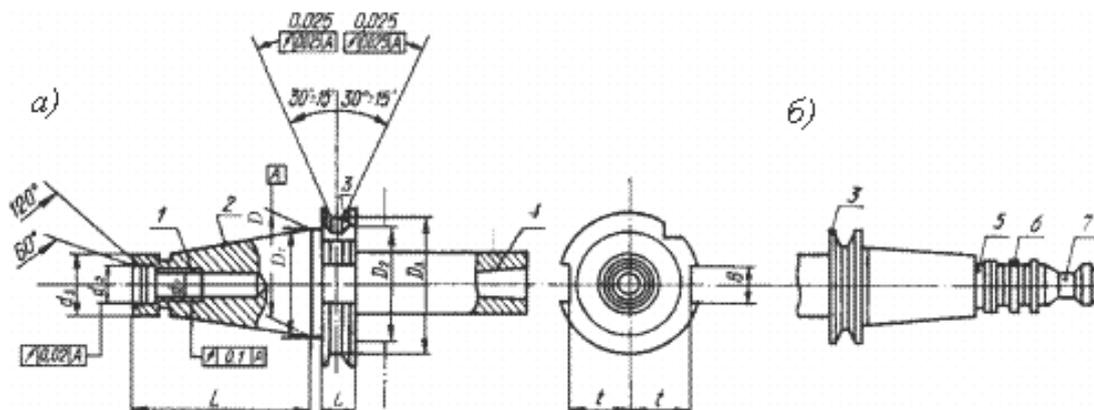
Оправка для многоцелевых станков с ЧПУ: а – хвостовик; б – хвостовик с кодовыми кольцами
